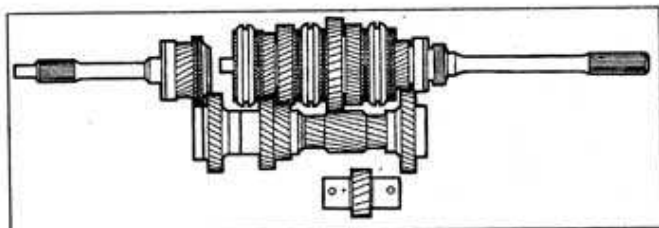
Валы и шестерни коробки передач после их сборки
